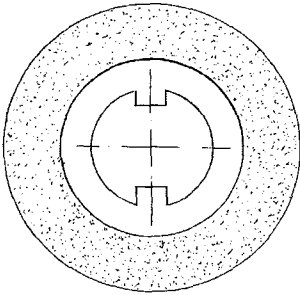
Тарельчатая пружина с абразивным покрытием и двумя шлицевыми выступами.
